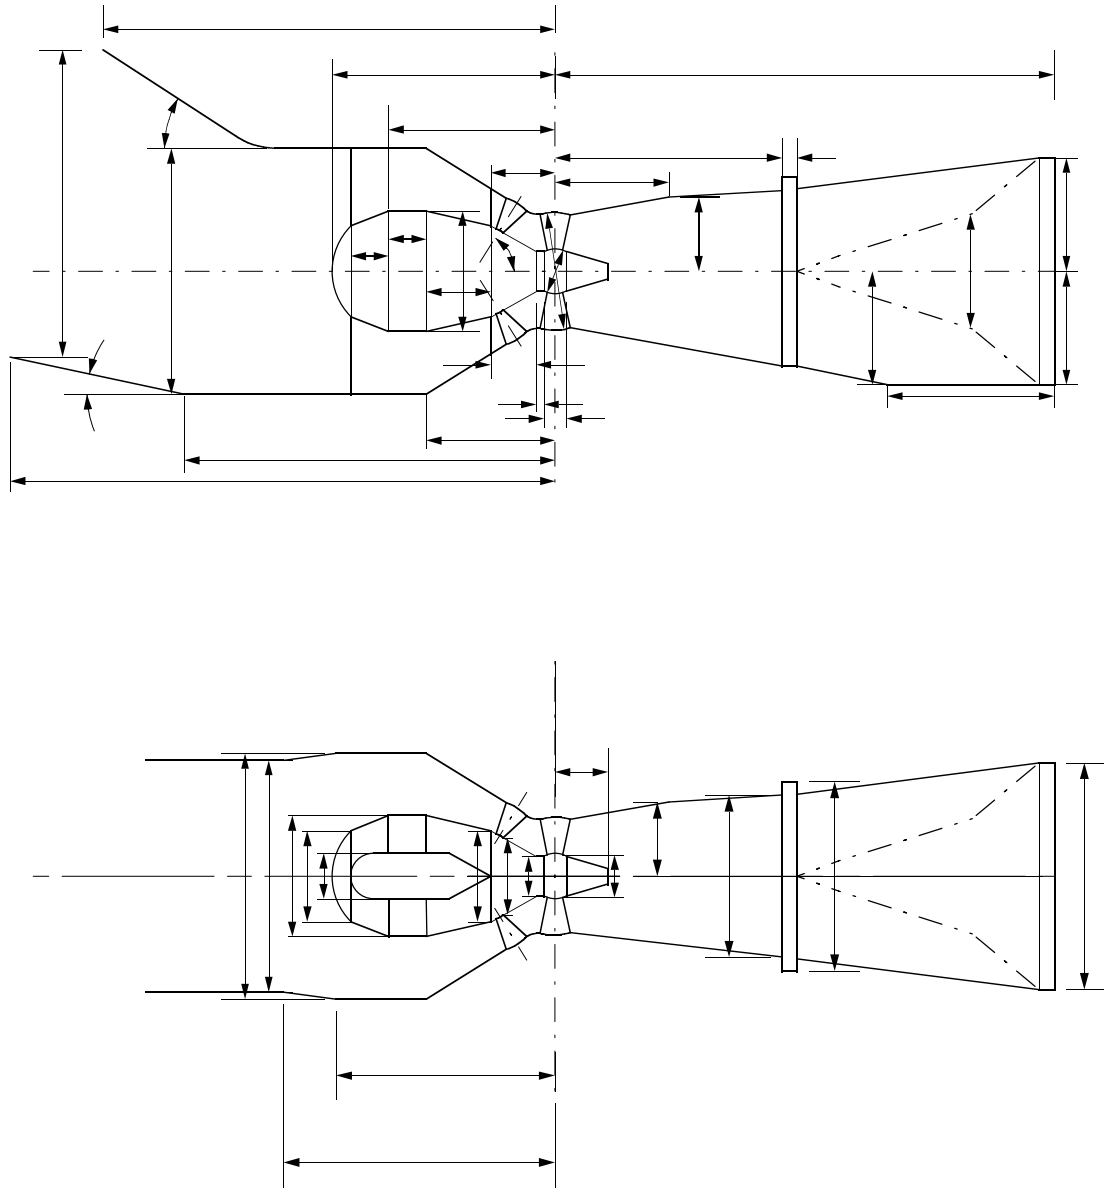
Exemple des dimensions à contrôler sur un groupe bulbe
